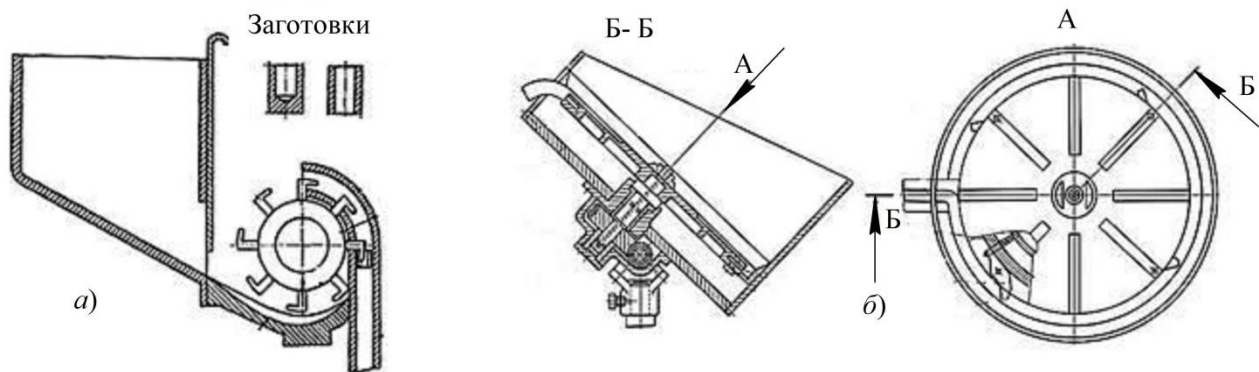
Бункера: *a* – с крючковым механизмом для загрузки колпачков и втулок с $L > d$; *б* – дисковый щелевой (для загрузки стержневых деталей с головками
